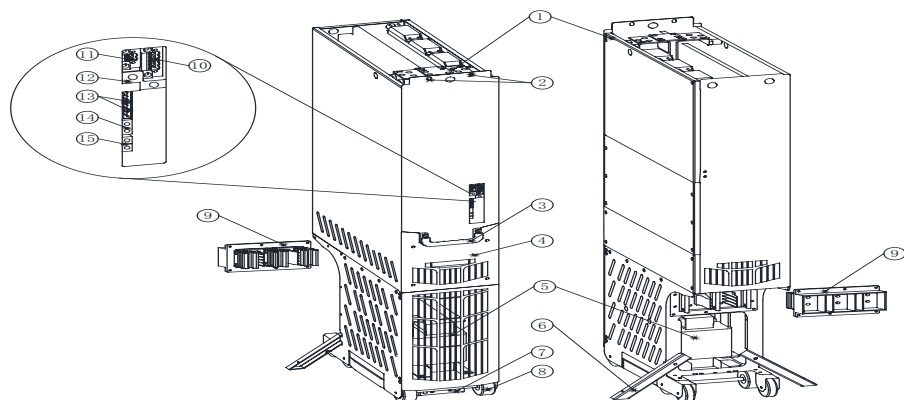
Конструкция инвертора типоразмера Н8.
